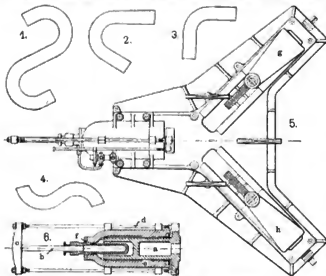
Z. A.: Hydraulische Rohrbiegemaschine.
